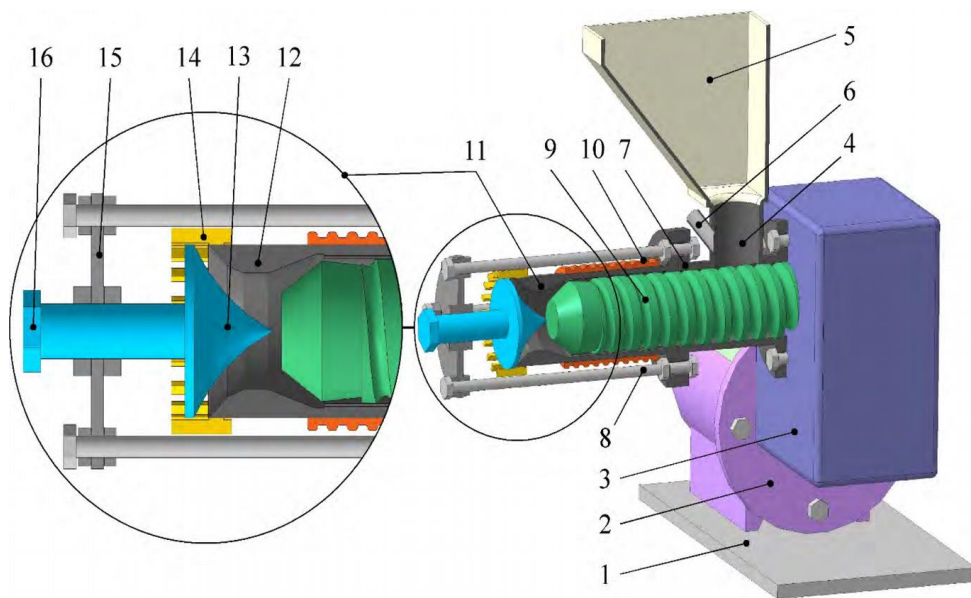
Конструктивно-технологічна схема експандера для виробництва комбікормів: 1 – опорна рама; 2 – асинхронний електродвигун; 3 – редукторний вузол; 4 – живильний механізм; 5 – завантажувальний бункер; 6 – патрубок подавання пари; 7 – робочий циліндр; 8 – напрямний елемент; 9 – гвинтовий робочий орган; 10 – нагрівальний елемент; 11 – формувальна насадка; 12 – звужена ділянка; 13 – увігнутий конус; 14 – корончата фіксувальна гайка; 15 – напрямна пластина; 16 – кріпильна гайка.
